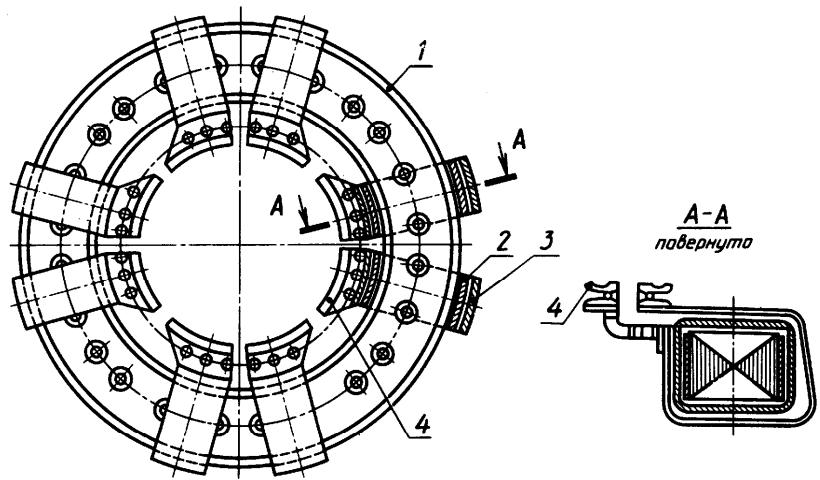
Схема кольцевого трансформатора для стыковой контактной сварки труб больших диаметров
